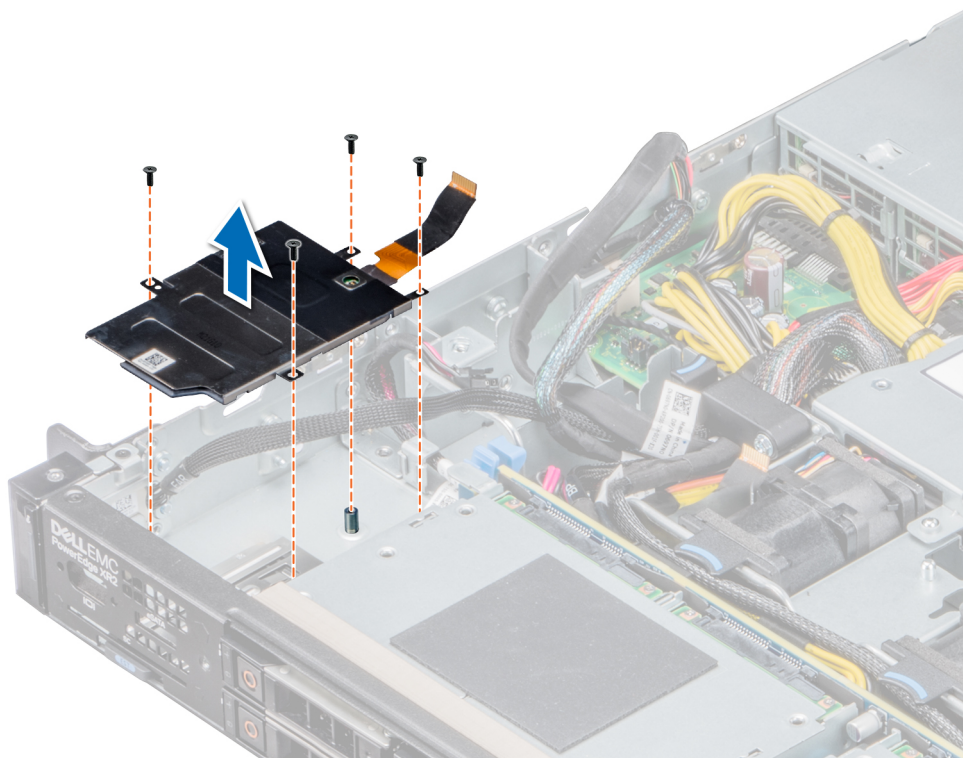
Entfernen des Smart Card-Lesegeräts
